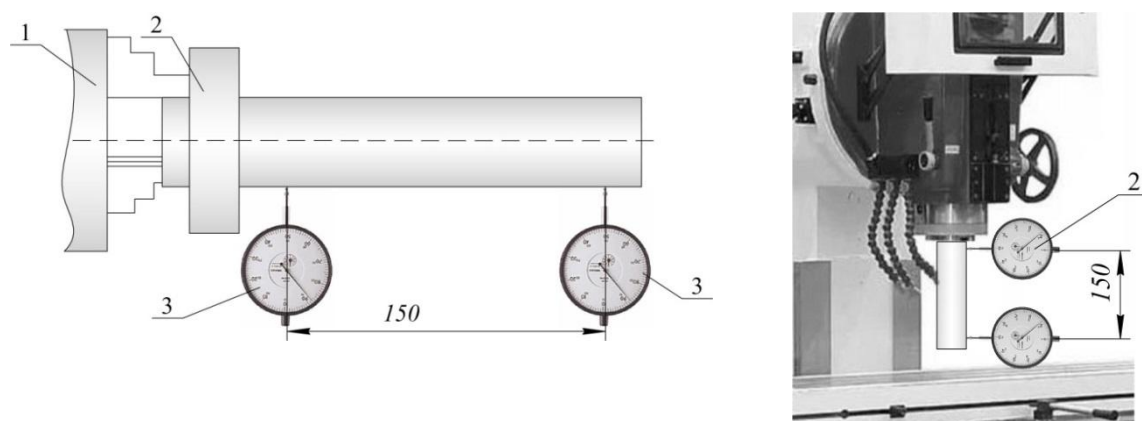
Схема контроля радиального биения шпинделя: *а* – шпинделя токарного станка; *б* – шпинделя вертикально-фрезерного станка
